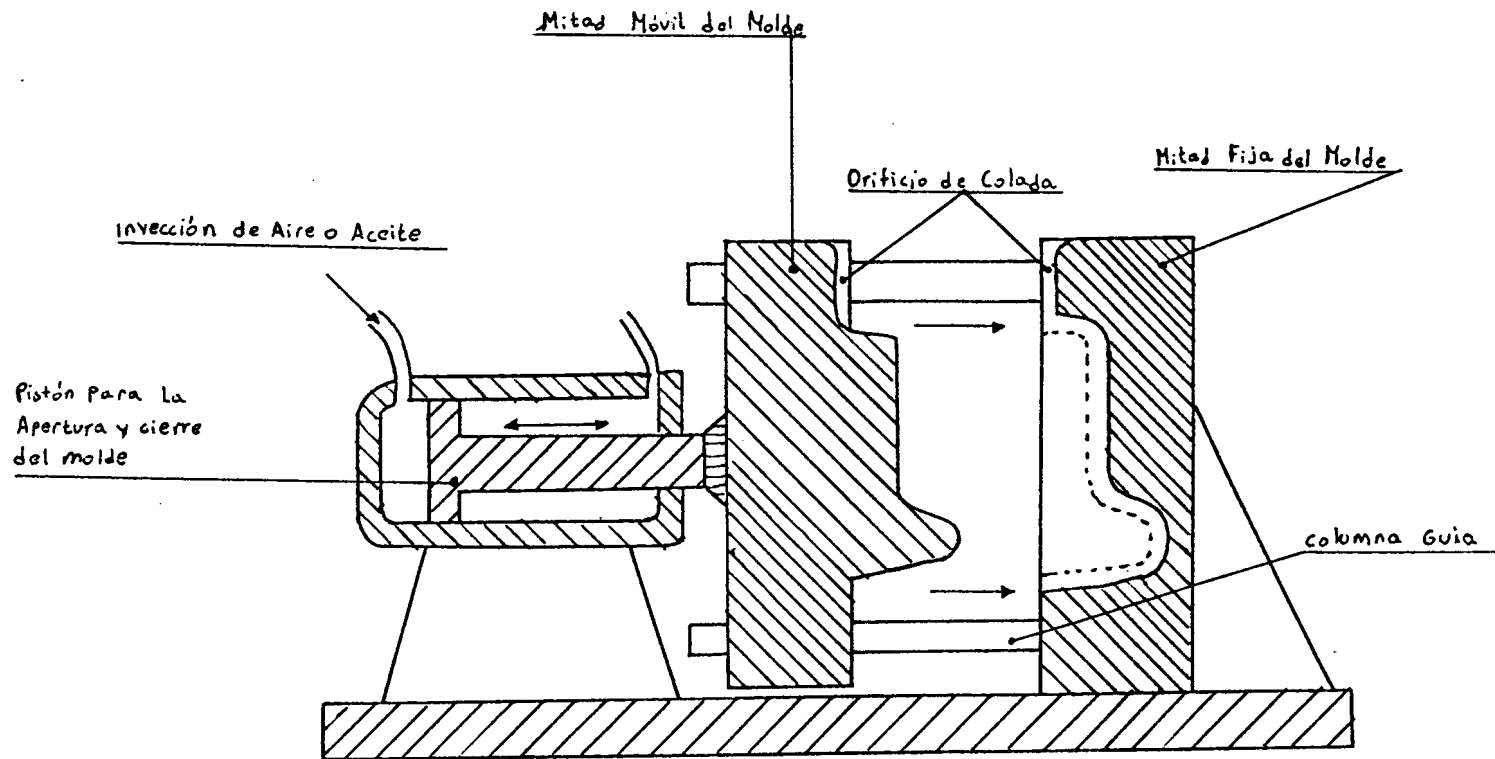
FUNDICION EN MOLDE PERMANENTE
